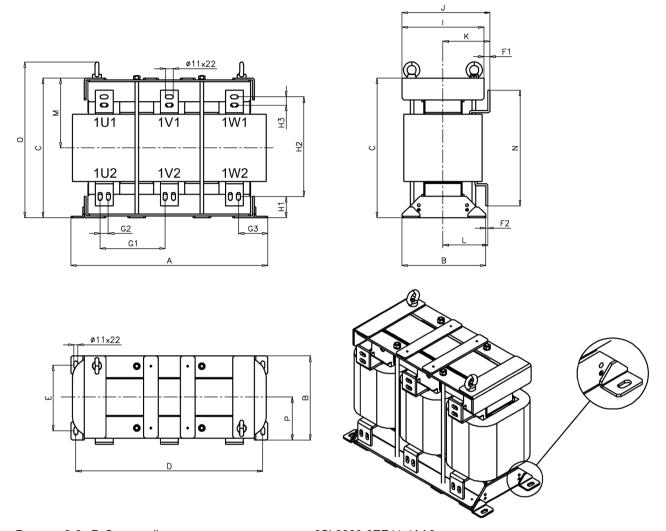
Габаритный чертеж сетевого дросселя 6SL3000-0EE41-4AA0
